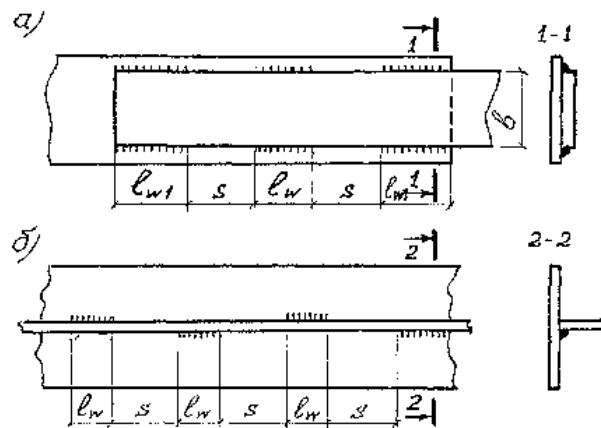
Схема переривчатих кутових зварних швів:
